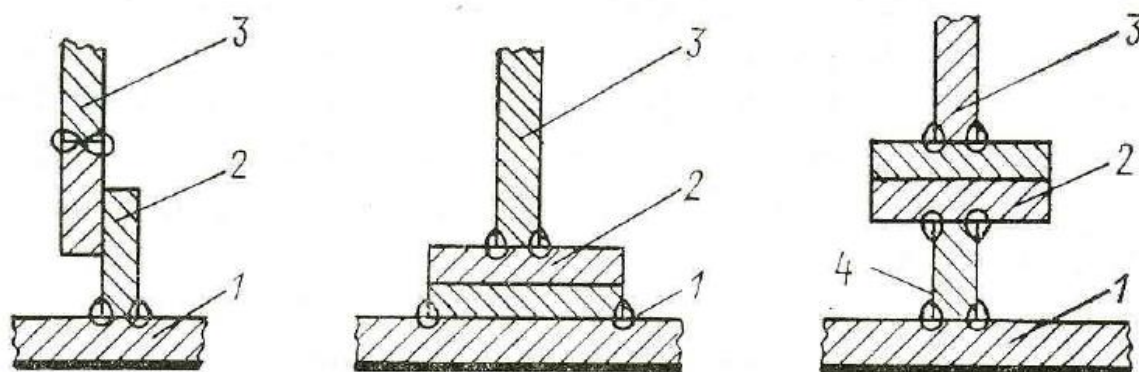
Типы сварных соединений через биметаллические переходники:
